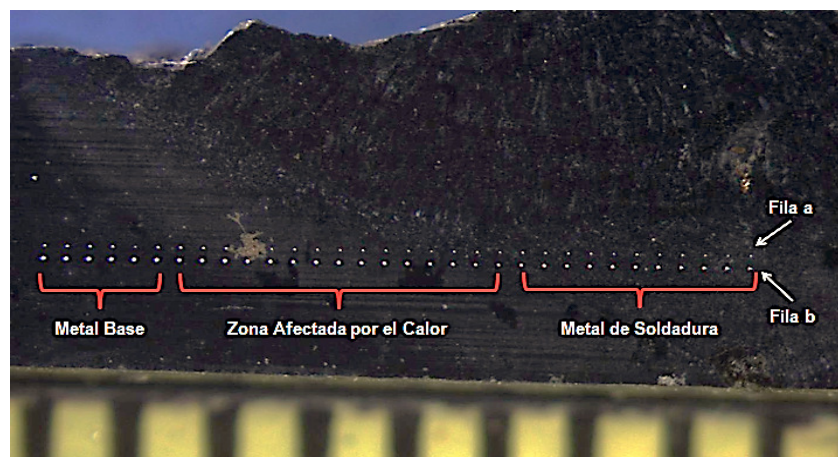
10 Perfil de indentaciones sobre placa soldada
